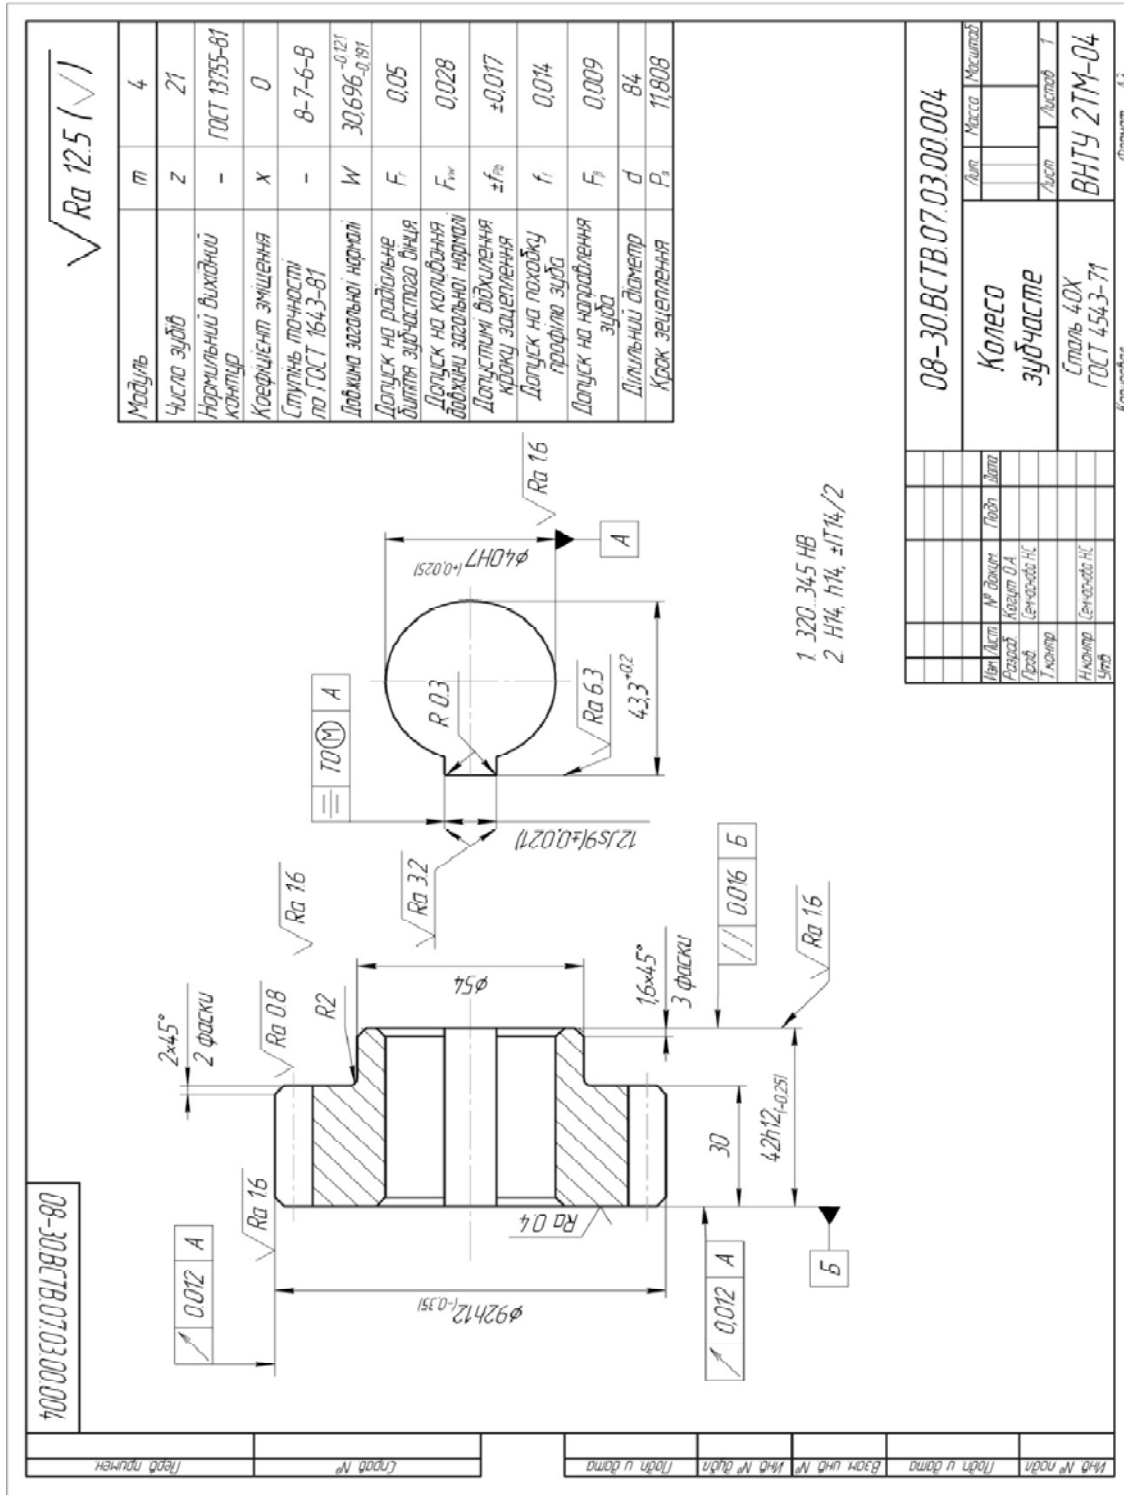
Приклад робочого креслення зубчастого колеса
